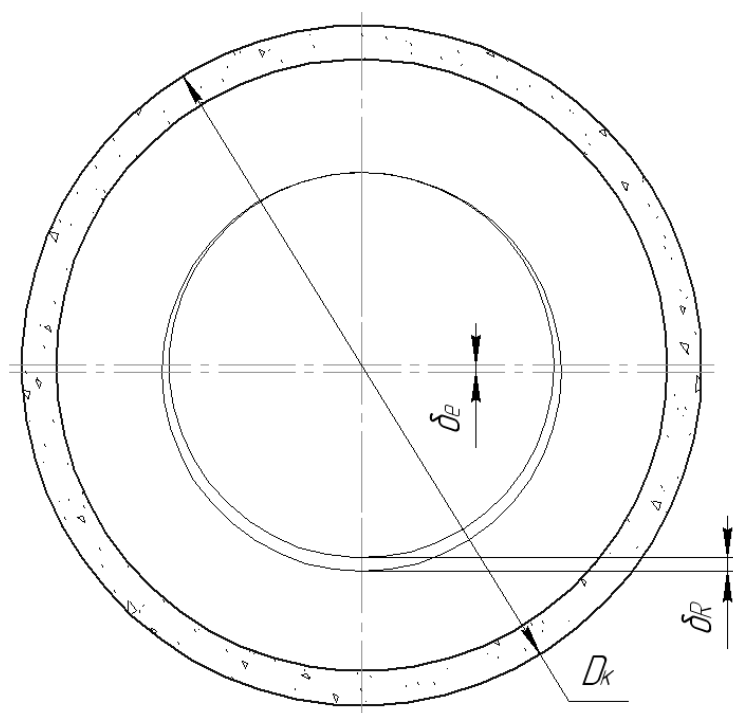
Расчетная схема к определению радиального биения при установке круга на фланцы
